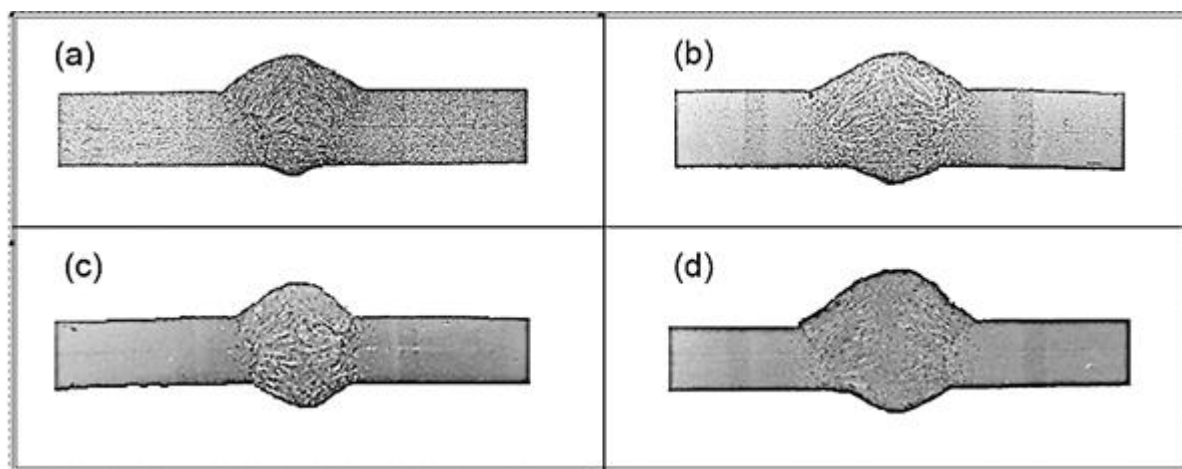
Fotomicrografias das juntas soldadas nos diferentes conjuntos de amostras de metal de base com metal de solda
